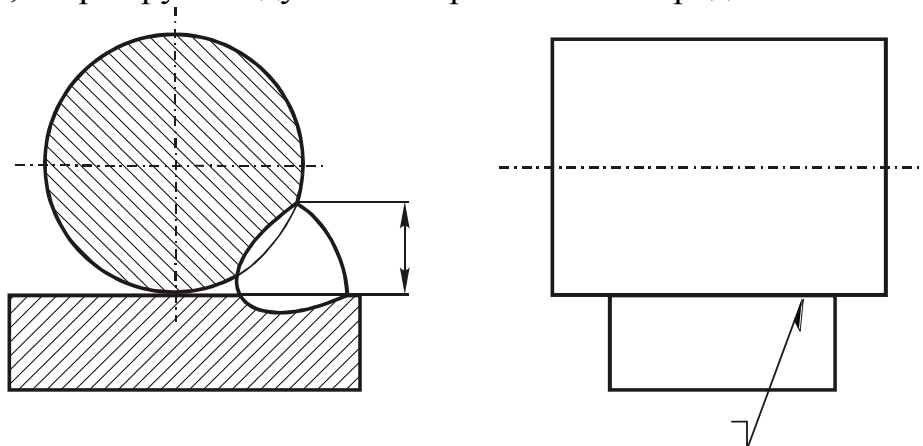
Обозначение нестандартного сварного шва
